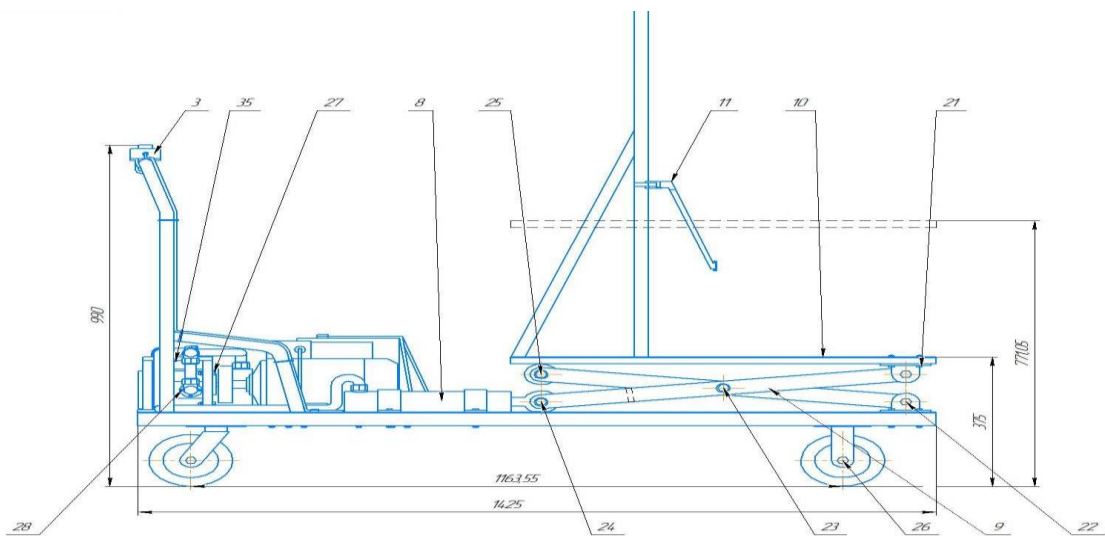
Схема разрабатываемого образца (вид спереди)
